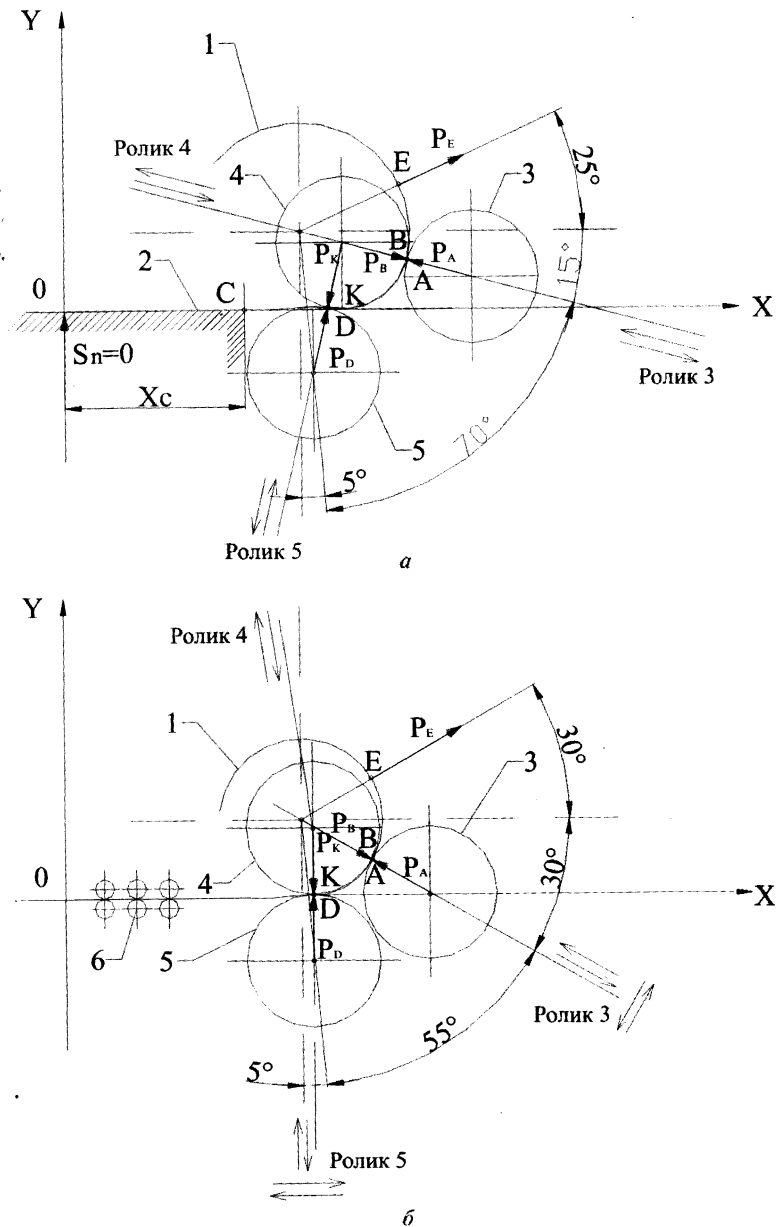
Принципиальные схемы работы блока гибочных роликов станков для навивки спиралей при производстве поршневых колец: а – станок Б042 конструкции НИИТТиСМ; б – станок С806 конструкции ОЗПК
